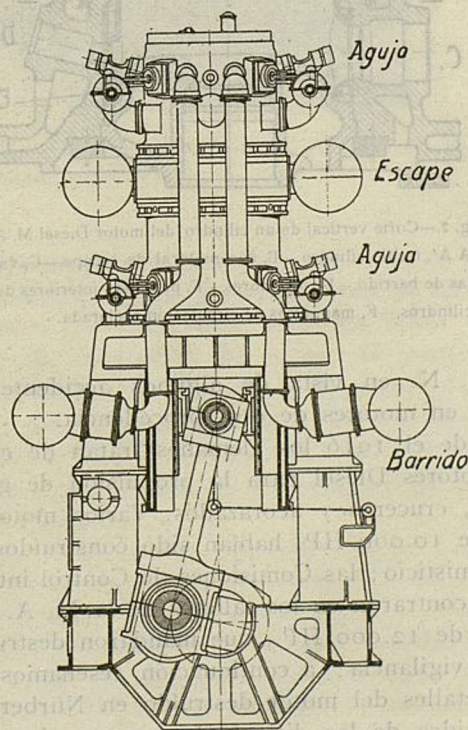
Vista de frente del motor Diesel M. A. N.,
